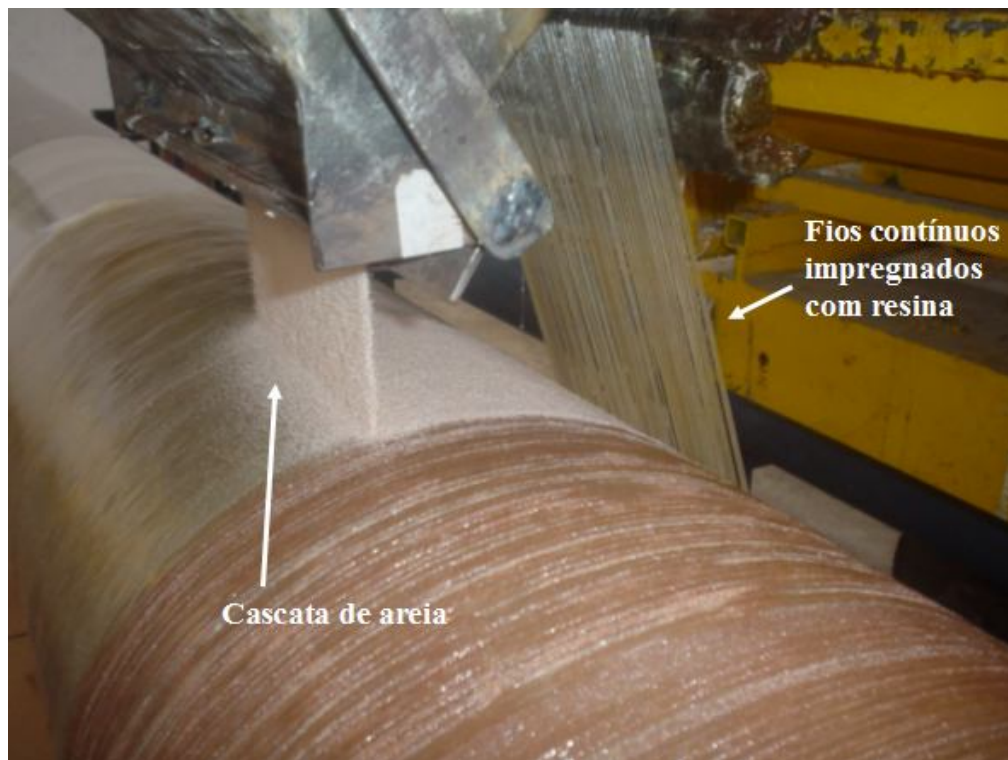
Processo de fabricação da estrutura do tubo [13].
